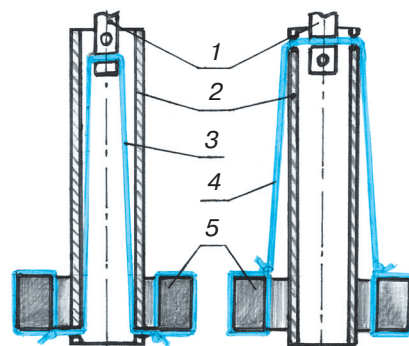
Схема привязи груза при сборке: 1 — змейка; 2 — цилиндр; 3 — нить А; 4 — нить Б; 5 — груз.
